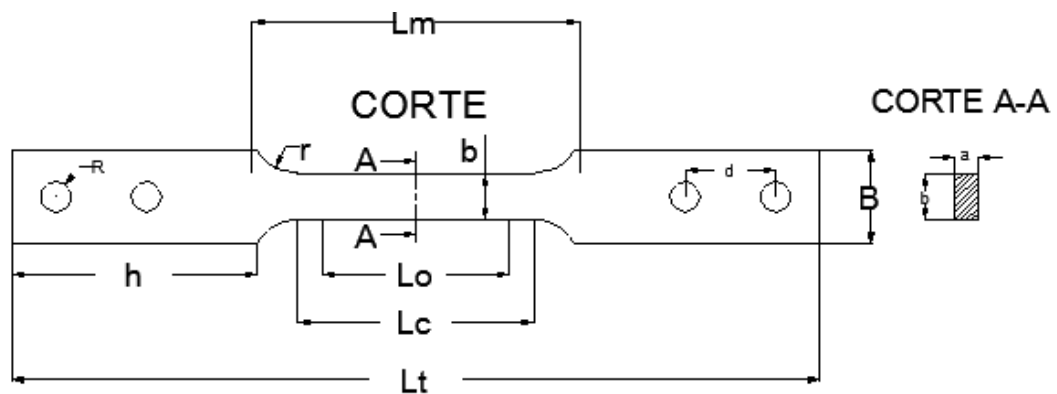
Esquema del espécimen plano de sección reducida para los ensayos
